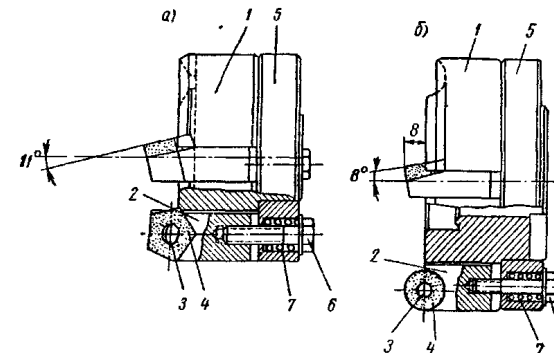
Торцовая фреза с многогранными пластинками
